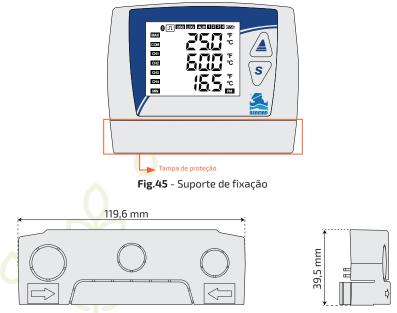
Dimensões da tampa de proteção das conexões e cavidades destacáveis
